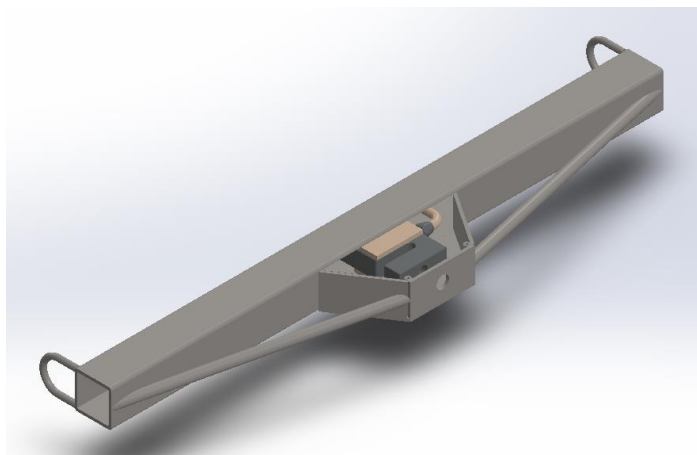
segundo protótipo desenho inicial - Vista isométrica
